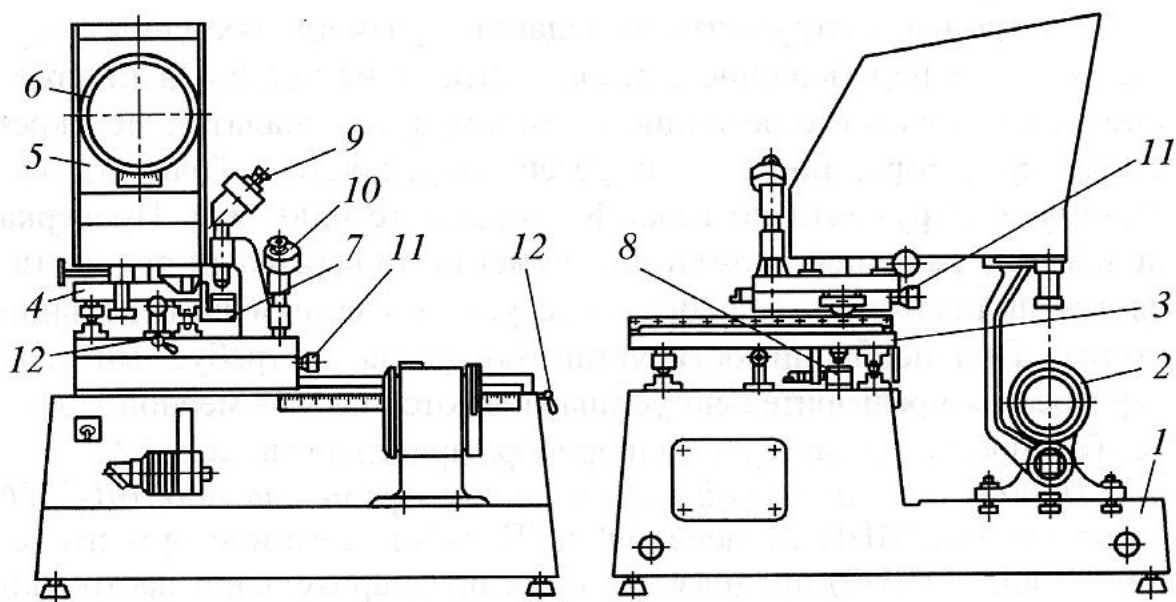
Прибор для размерной настройки инструментальных блоков токарных станков
